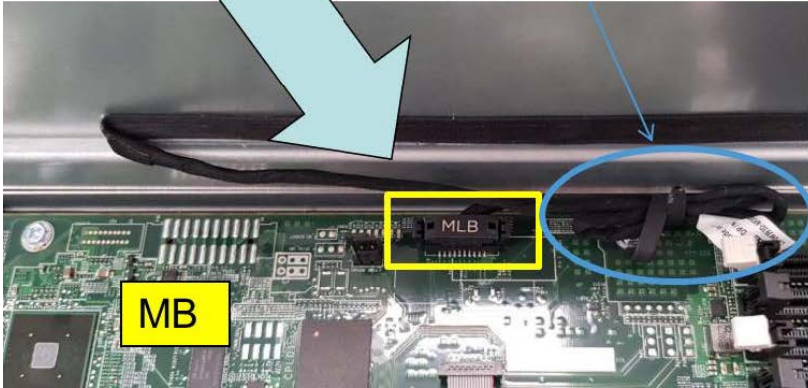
Placa de control del ensamblaje del cable de control frontal a MB
